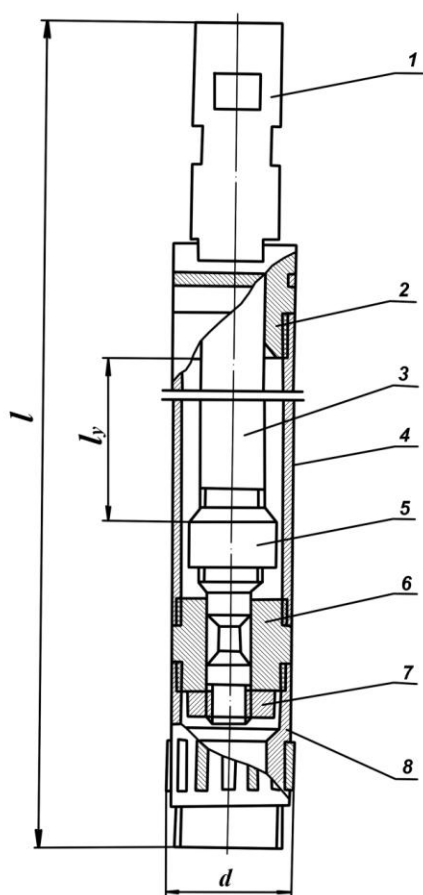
Схема ударного отсоединительного снаряда УС-1: 1 – верхний переходник; 2 – переходник-наковальня; 3 – шток; 4 – корпус; 5 – ударник; 6 – ниппель; 7 – гайка; 8 – нижний переходник; d – наружный диаметр; l – длина; l_y – ход ударника относительно наковальни
